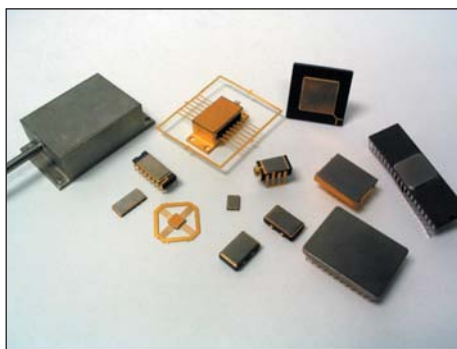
Примеры корпусов, герметизируемых установкой шовно-роликовой сварки
